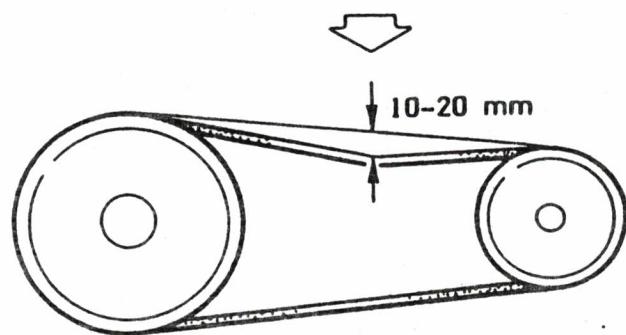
Keilriemenspannung, Drucklufterzeuger (EliMot)
